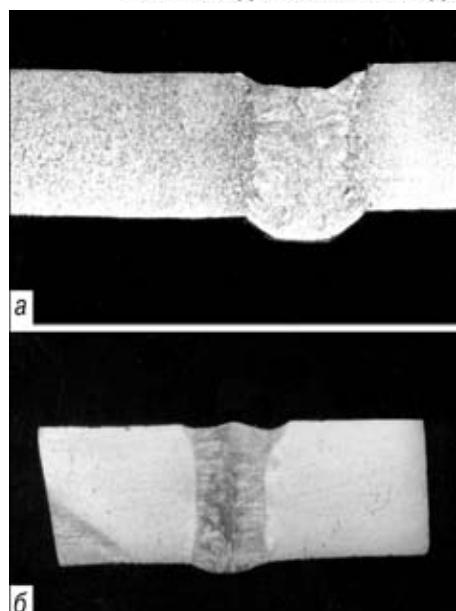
Сварной шов, выполненный сваркой ATIG без присадочной проволоки: а – без автоопрессовки; б – с автоопрессовкой
